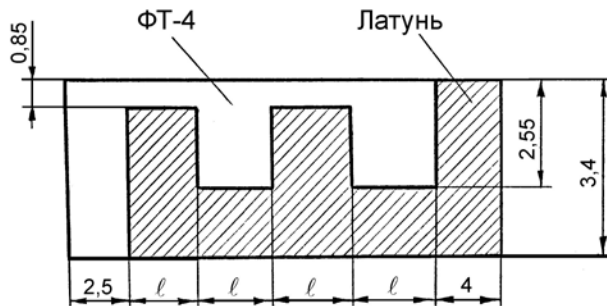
КЗ-поршень из четвертьволновых отрезков линий с одинаковой длиной l и разным волновым сопротивлением (вид со стороны узкой стенки волновода)
